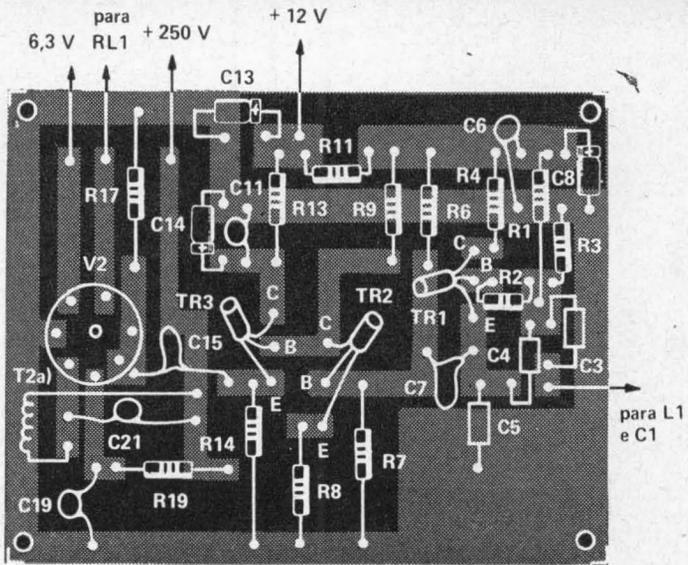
Disposição dos componentes do O.F.V. sobre a plaqueta da Fig. 4.
